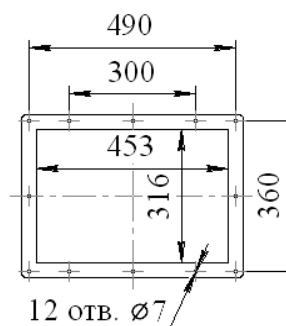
Вентиляторы ВПИ-PRU-560. Присоединительные размеры
